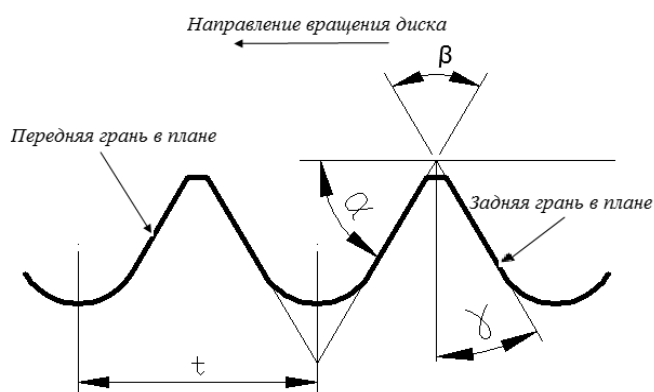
Режущие углы зуба дисковой пилы: α – передний угол; β – угол заострения; γ – задний угол; t – шаг зубьев
